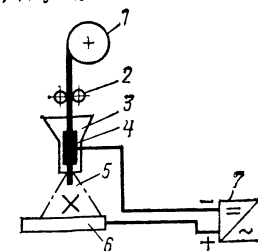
Принцип сварки: 1 — катушка с электродной проволокой; 2 — механизированная подача электродной проволоки; 3 — лоток для флюса; 4 — контактный мундштук; 5 — флюс; 6 — изделие с кабелем; 7 — источник питания
